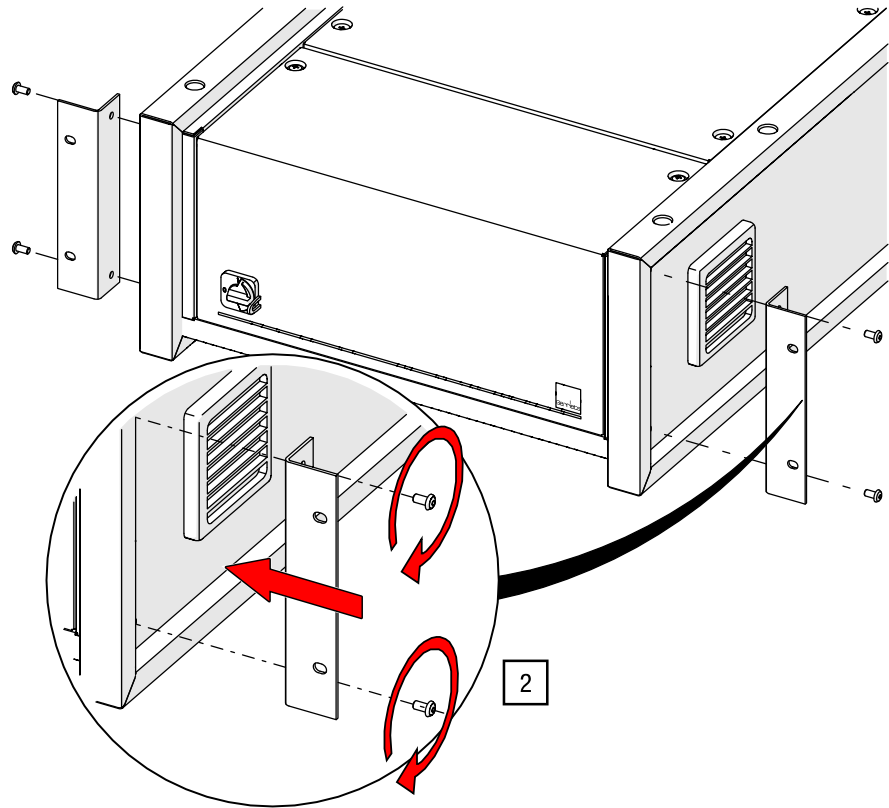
Rack-Montagewinkel anschrauben (Modell kann abweichen)
